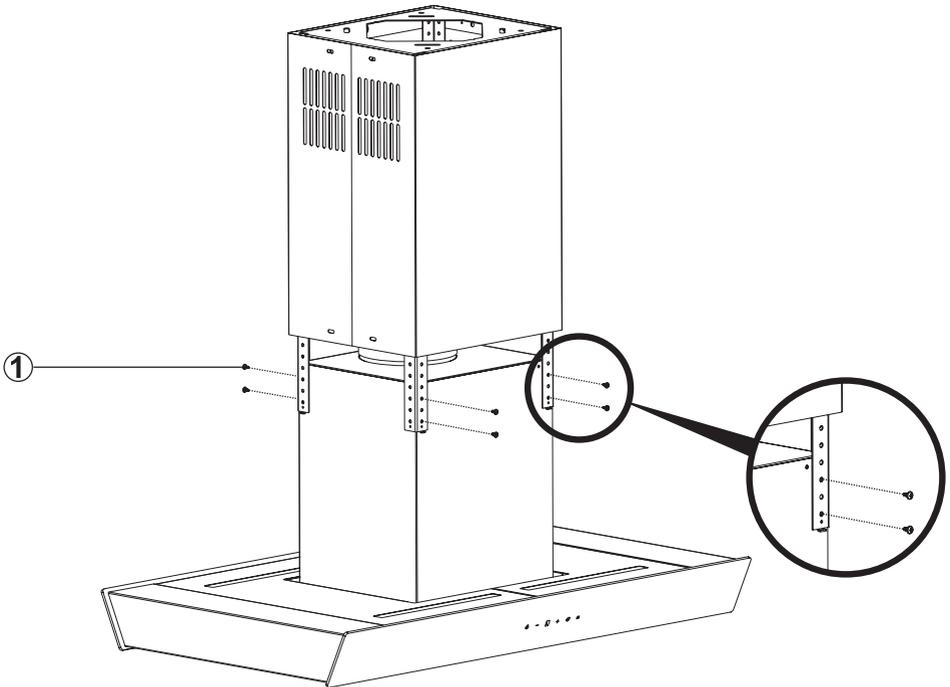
INSTALLAZIONE E COMPONENTI PARTE 4
